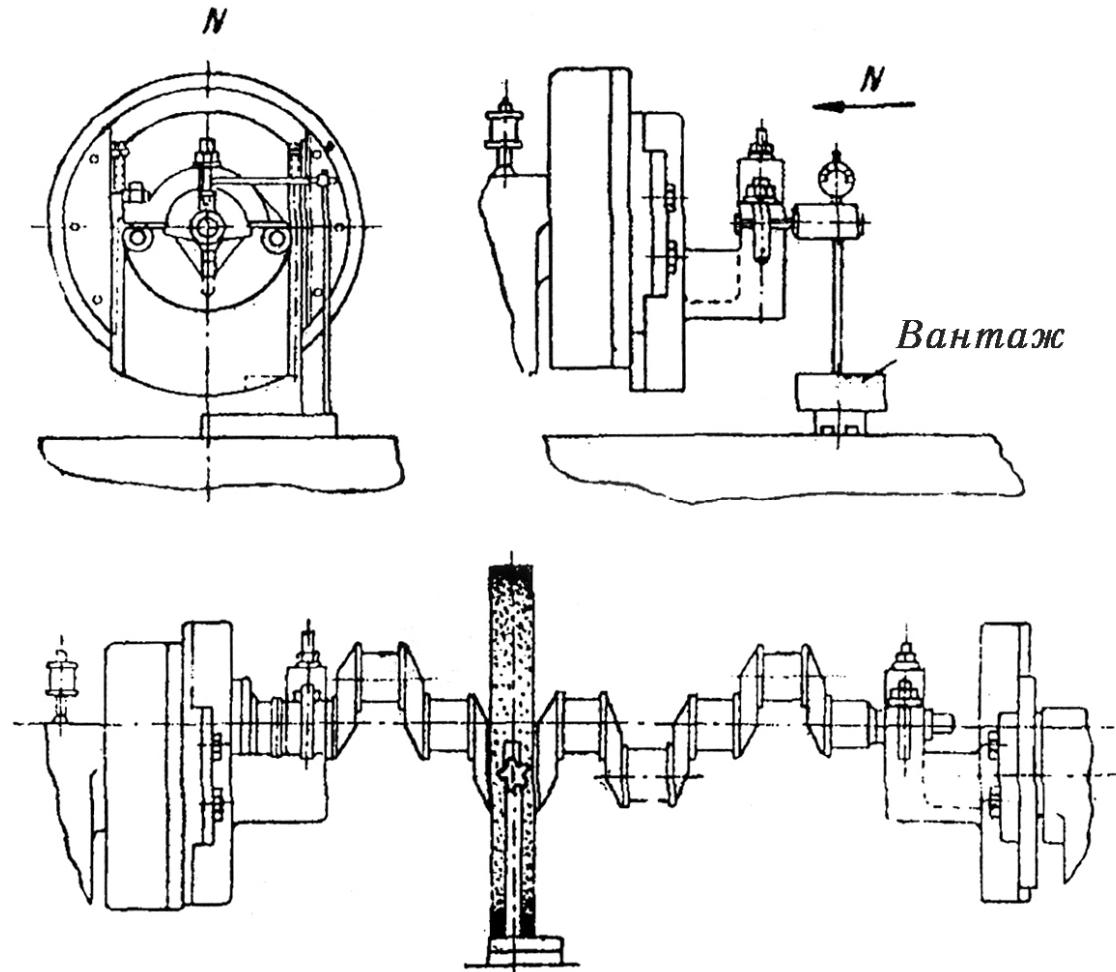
Схема установки вала для шліфування шатунних шийок
